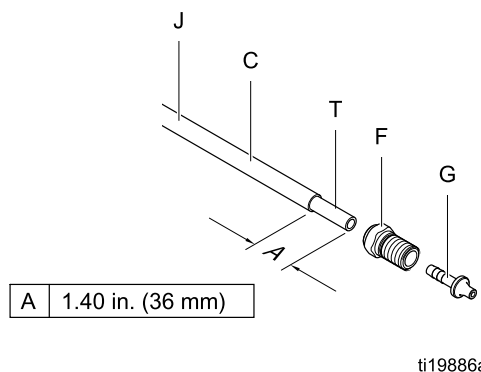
Dimensions du flexible non blindé 24M733 au niveau du pistolet
